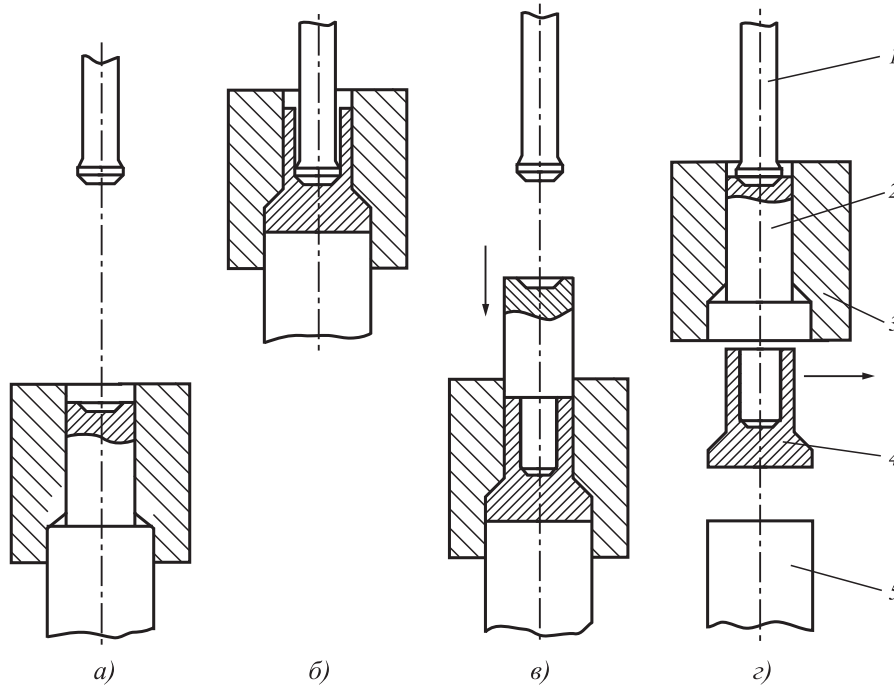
Последовательность перемещений инструментов, подачи заготовки и удаления изготовленной детали при выдавливании на специализированном прессе
